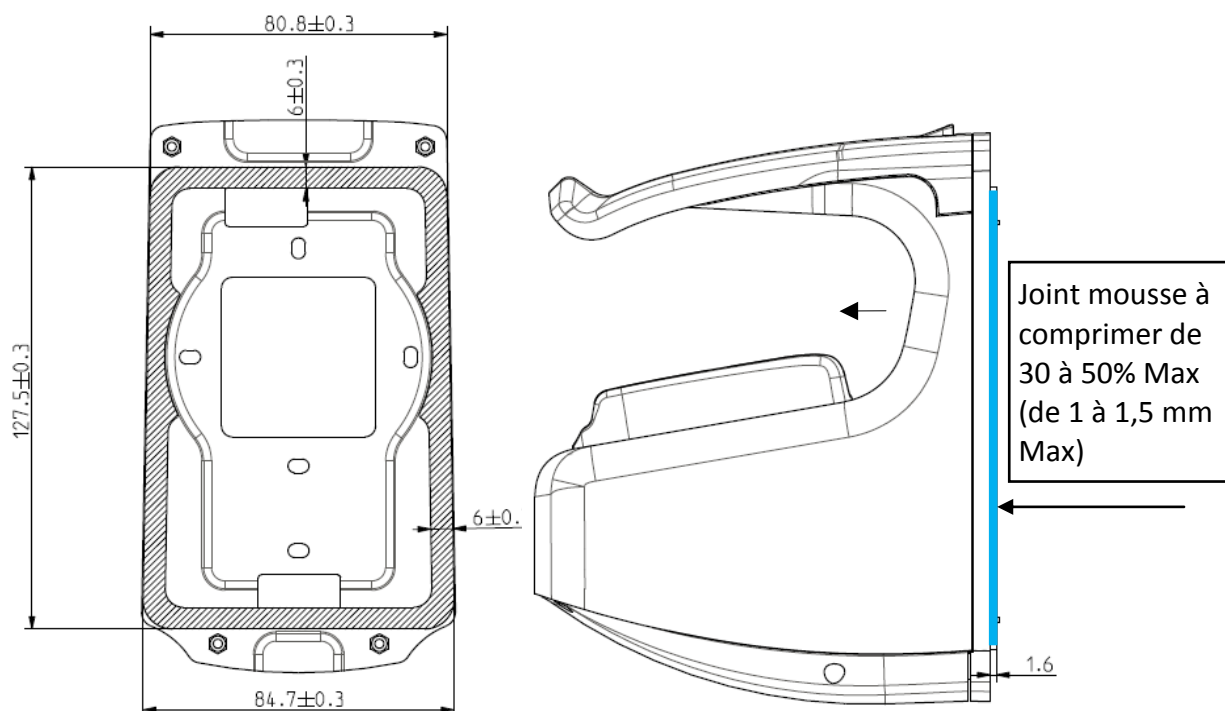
Joint d'étanchéité tôle murale / entretoise
